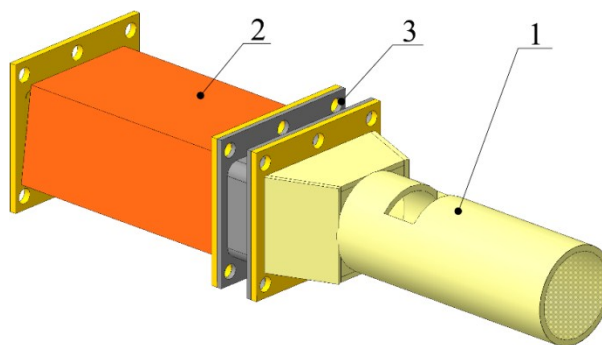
Конструкция впускного воздушного коллектора: 1 – воздушный патрубок; 2 – камера предпускового подогрева воздуха; 3 – вентилятор
